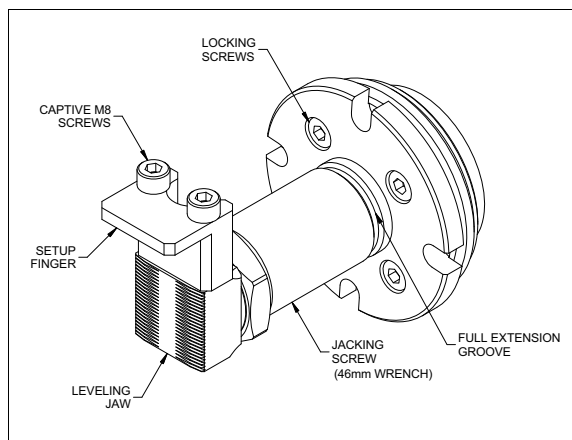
DÉTAILS DES JAMBES DE SERRAGE DU MANDRIN DI
